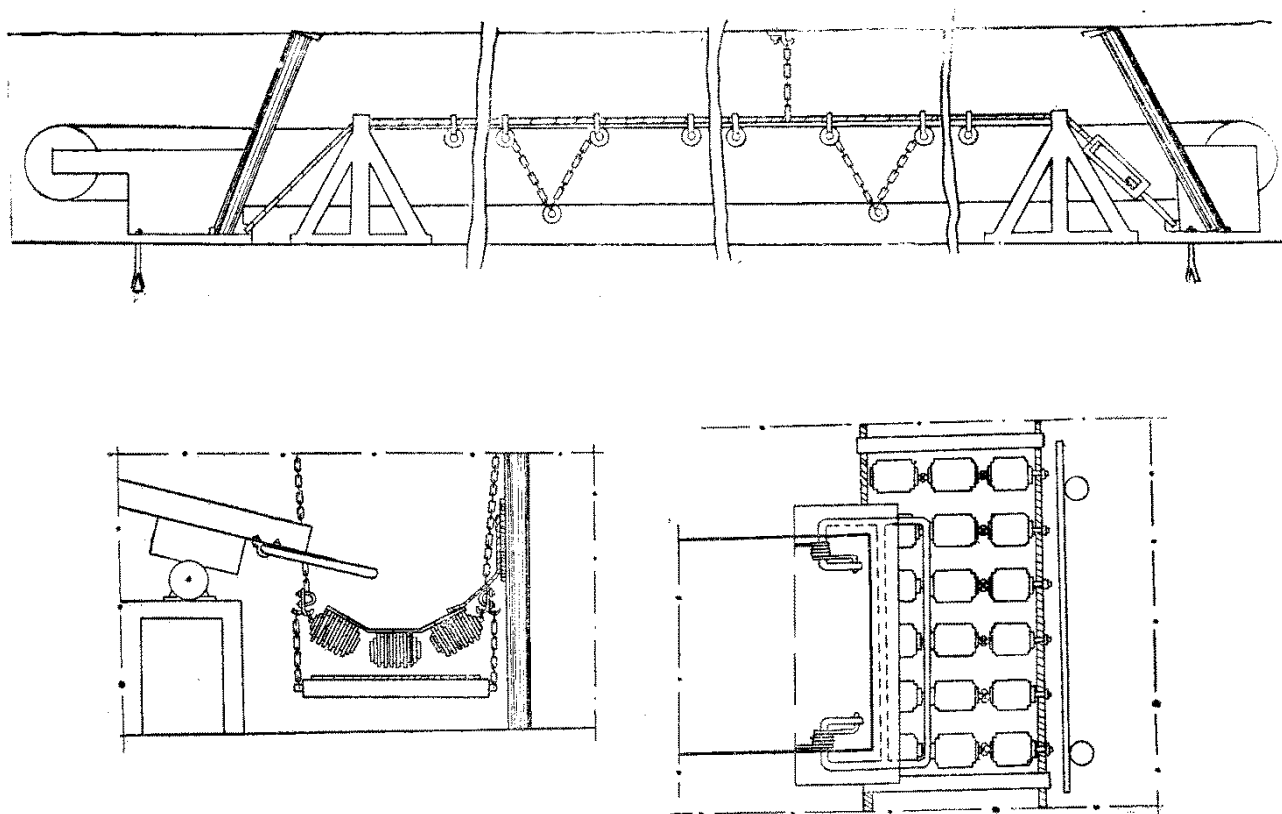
Принципова схема безрамного стрічкового конвеєра:
